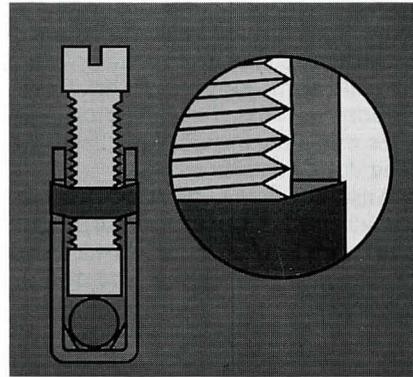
Die Ausführung des Gewindebalkens bewirkt mit zunehmendem Drehmoment eine elastische Verformung der Klemmkörper-Seitenwände (Schraubensicherung)
